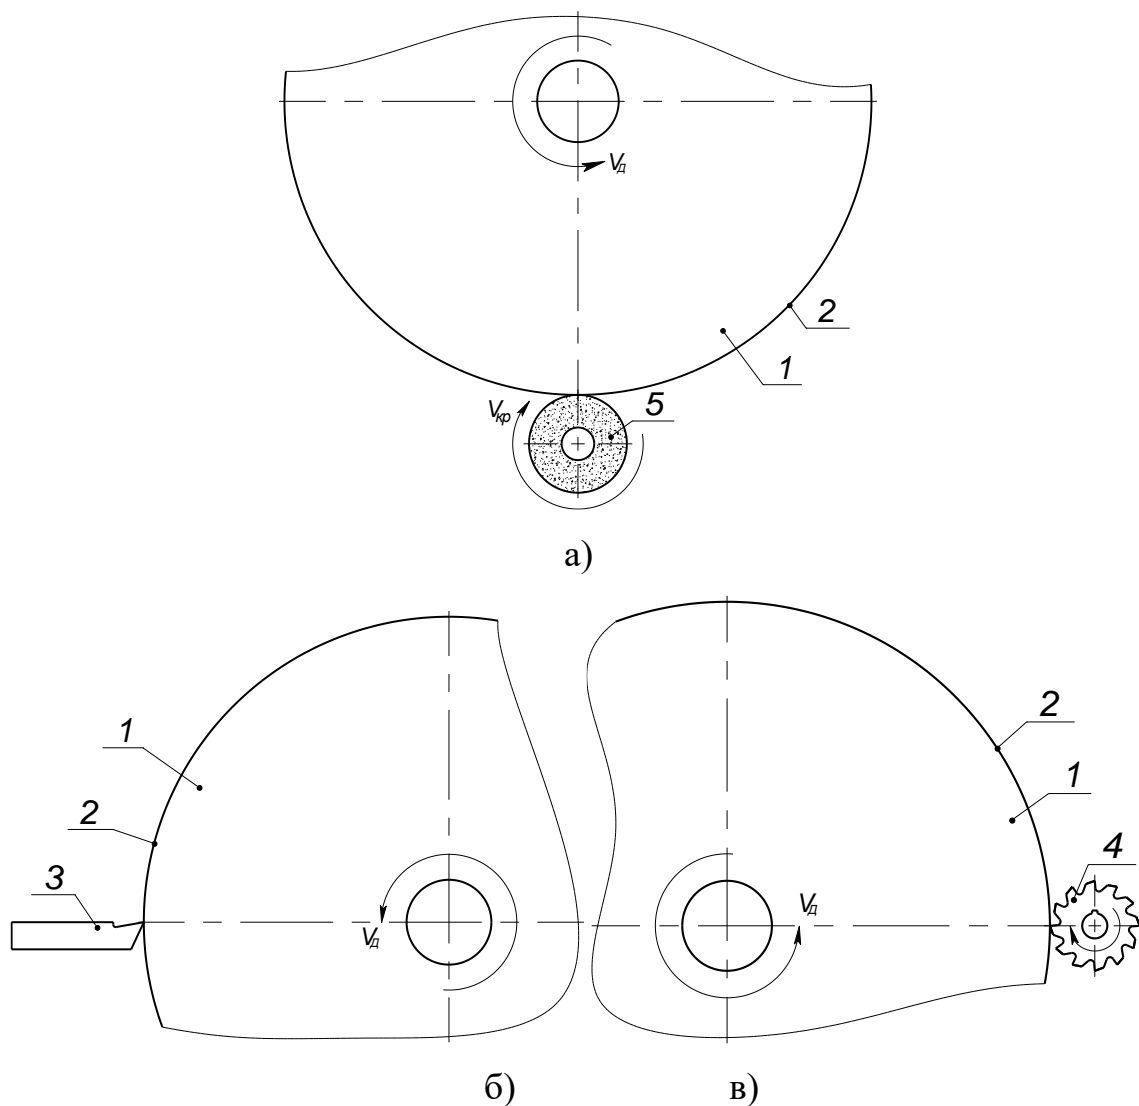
Комбинированный способ последовательной обработки колесной пары черновым шлифованием (а), точением (б) или фрезерованием (в) где 1 – колесная пара; 2 – обрабатываемая поверхность; 3 – резец; 4 – фреза; 5 – шлифовальный круг; V_d – направление вращения колесной пары; $V_{кр}$ – направление вращения шлифовального круга.
